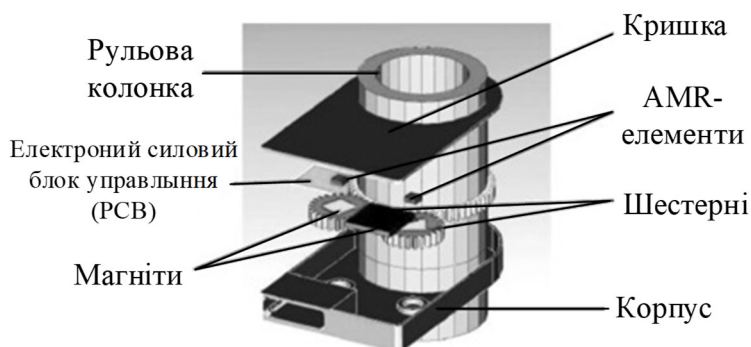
Конструкція датчика кута повороту рульового колеса, що працює за принципом анізотропного магніторезистивного вимірювання
